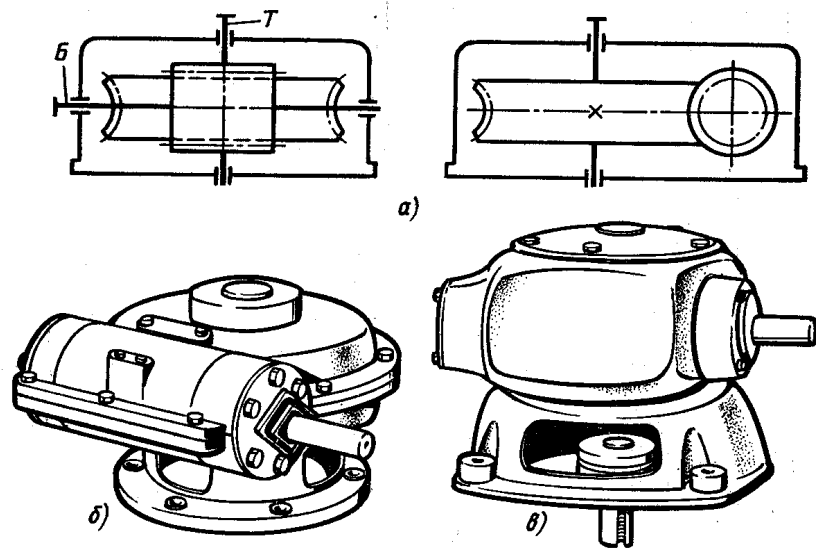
Червячный редуктор с вертикальным валом червячного колеса:
